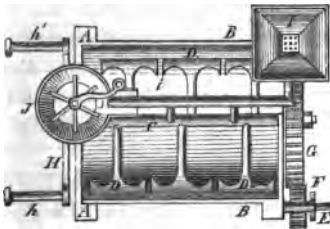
zeigt diese Maschine von vorn, Fig. 8 im Grundriss und Fig. 9 in der Endansicht. Dieselbe besteht aus einem hölzernen
